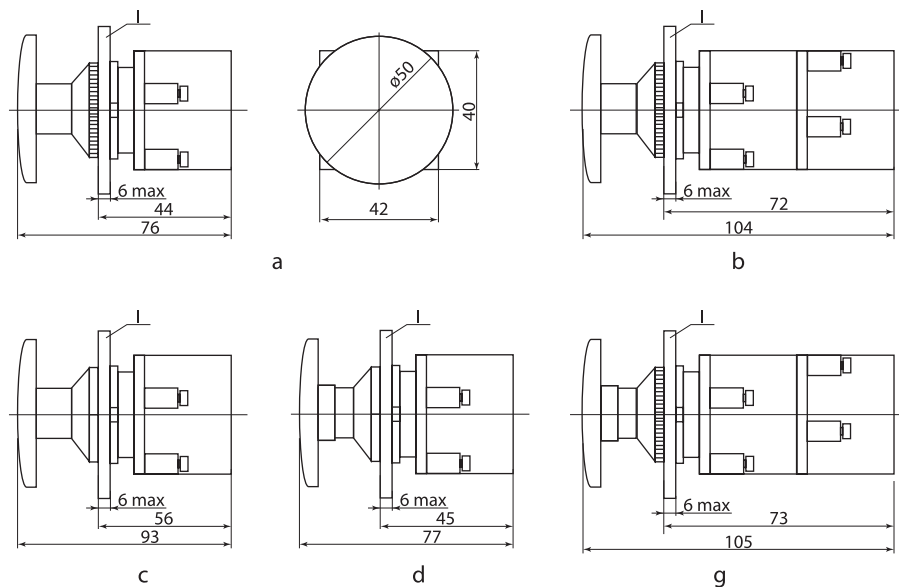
Габаритные и присоединительные размеры выключателей с цилиндрическим толкателем, l – панель (мм)
